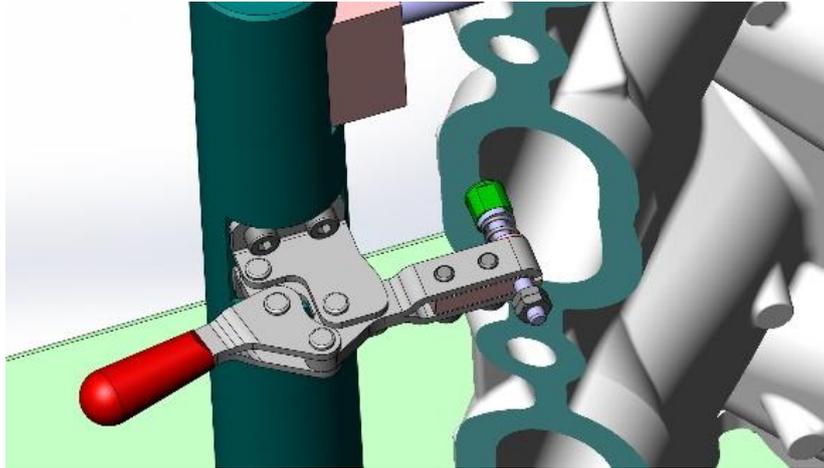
Clamp U-213 con sistema de capuchón plano
